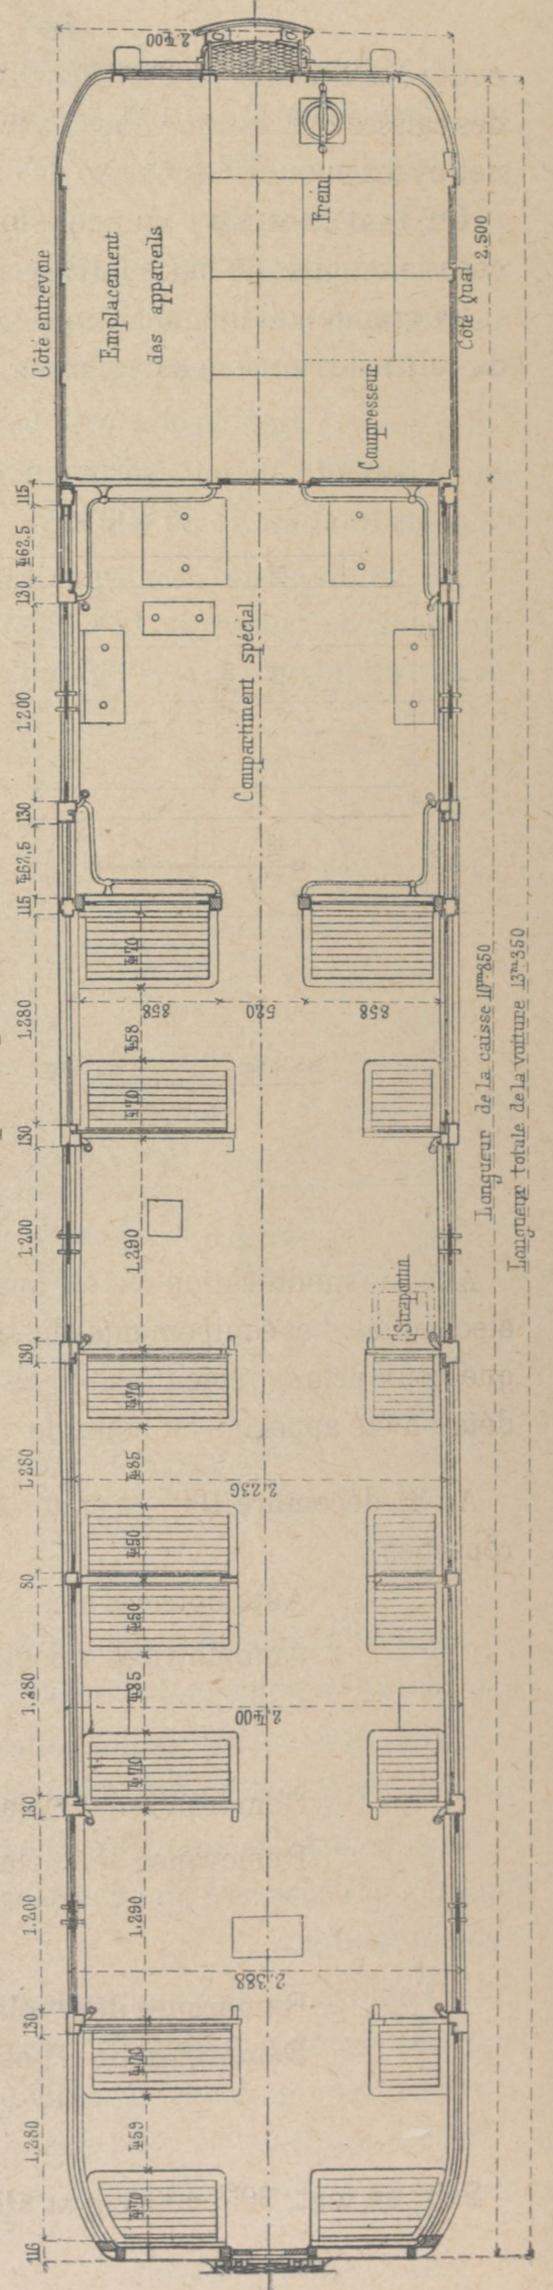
PLAN, ÉLEVATION ET COUPE LONGITUDINALE D'UNE VOITURE MOTRICE.
